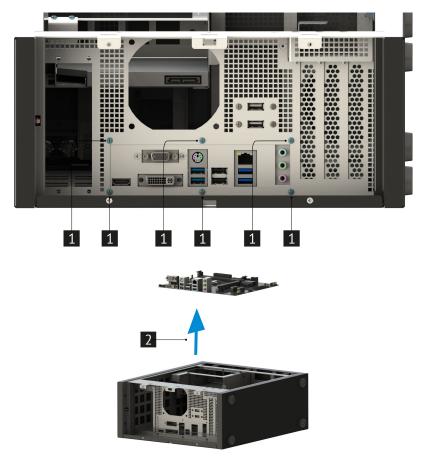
Извлечение материнской платы из корпуса рабочей станции
